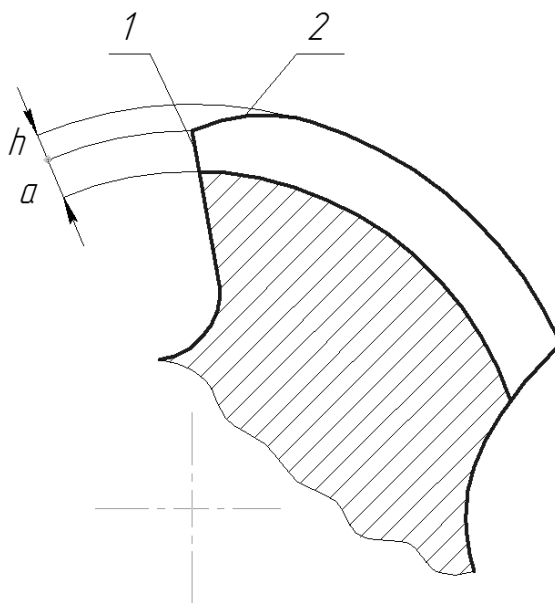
К задаче Б.9: зуб режуще-деформирующего метчика
